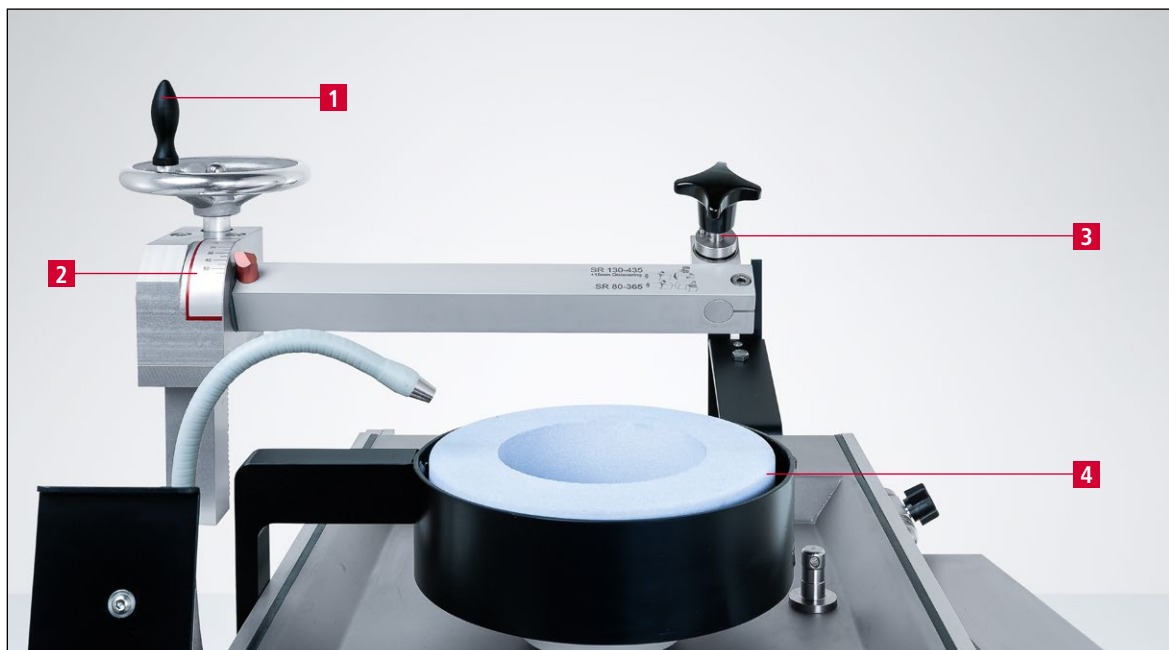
Поворотный рычаг HV 207, общий вид
